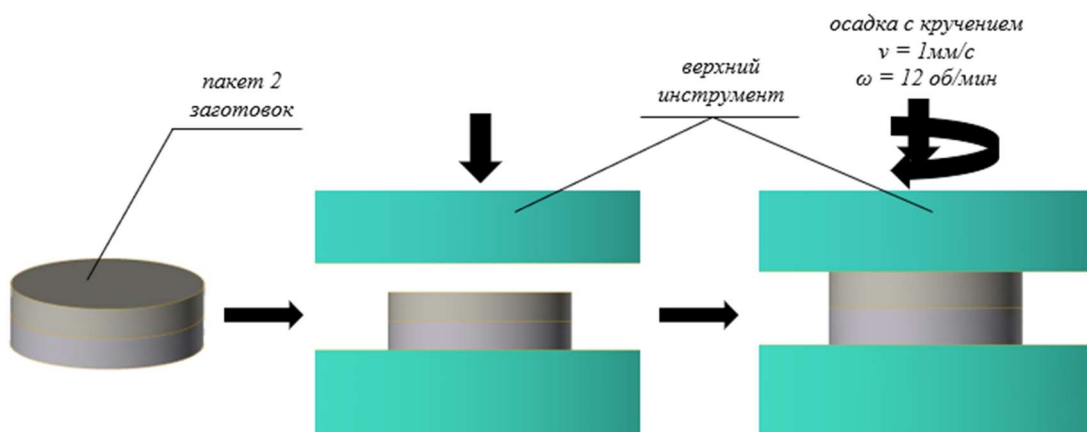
Схема осадки образцов из алюминиевых сплавов АМг2 и АМг6
